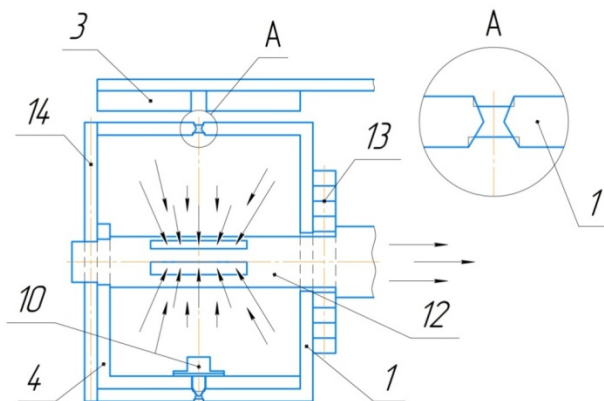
Схема высевающего барабана пневматического высевающего аппарата сеялки точного высева (вид спереди)
